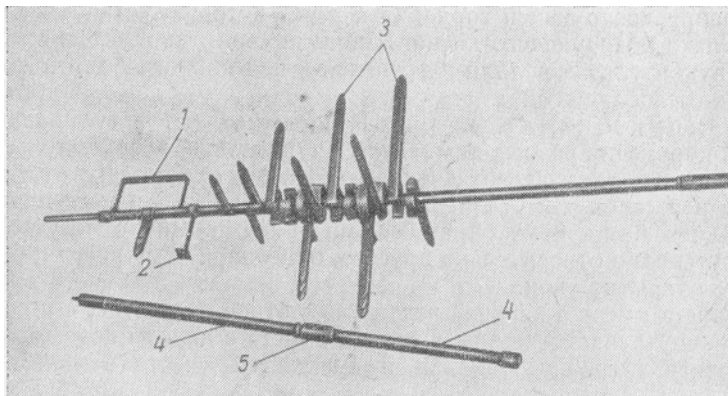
Мешалка с пружинными жесткими рыхлителями:
